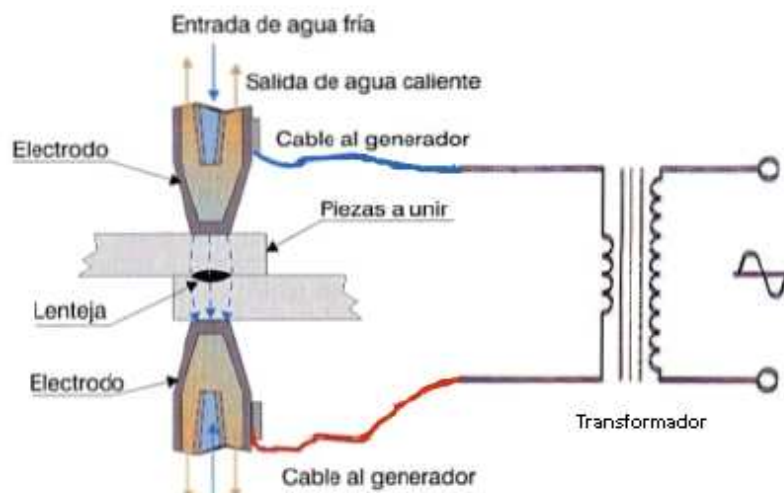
Equipo necesario para la soldadura por puntos
